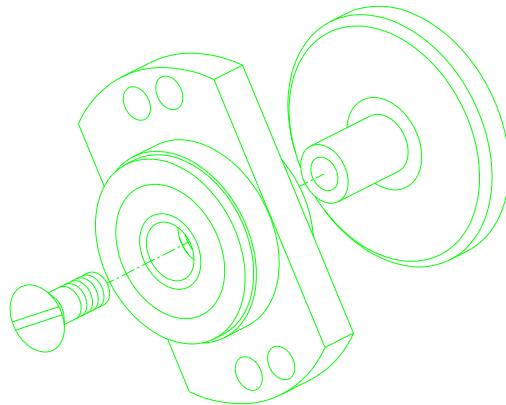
Сборка фланцевого планетарного держателя-шлифовального шпинделя
